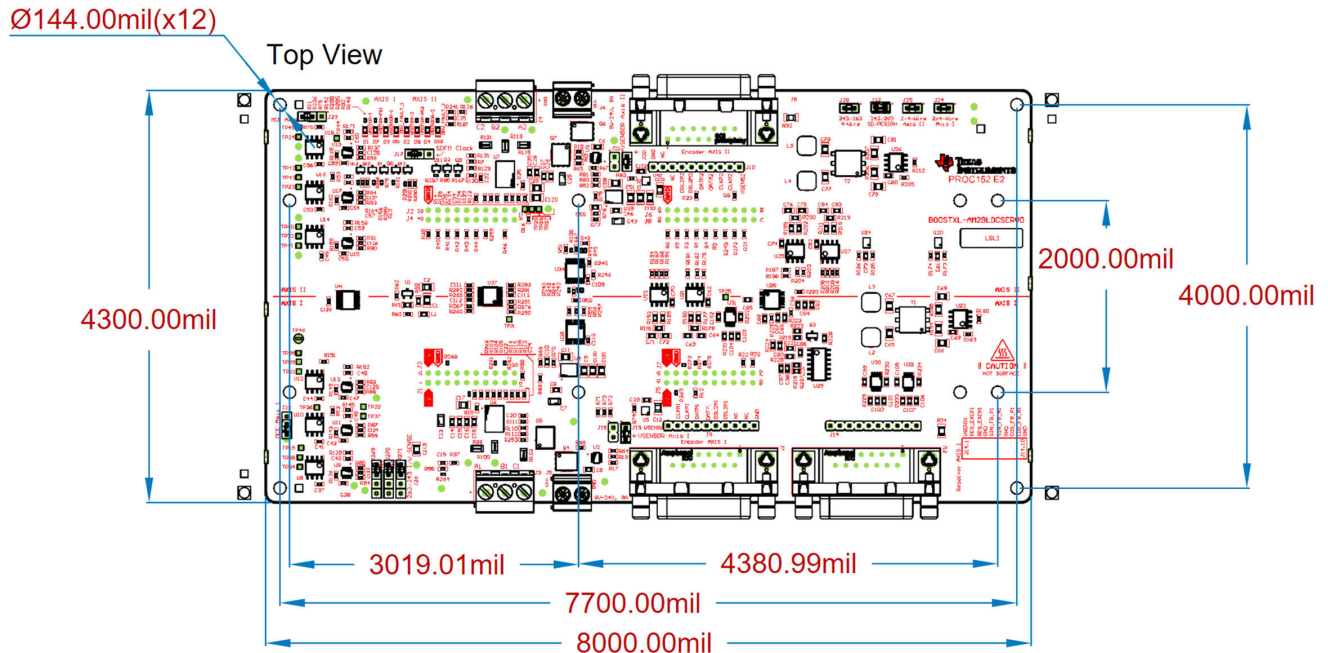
BP-AM2BLDCSERVO PCB 模组 - 顶视图
